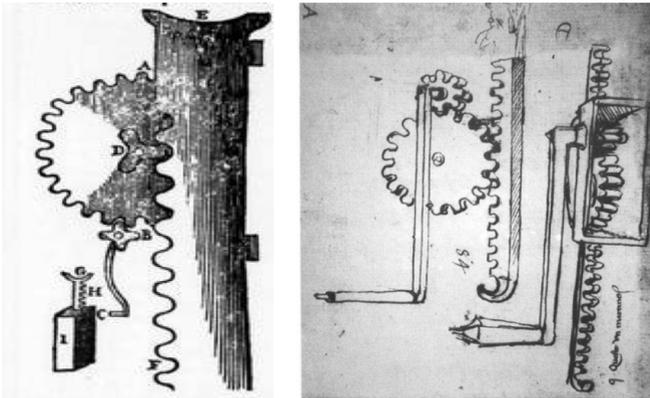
Слева чертеж механизма для преобразования вращательного движения в поступательное, сделанный Галилео Галилеем¹⁹, а справа – Леонардо да Винчи²⁰. Эта машина состоит из кривошипа, понижающей передачи и стержня с зубцами, который движется вверх и вниз.
